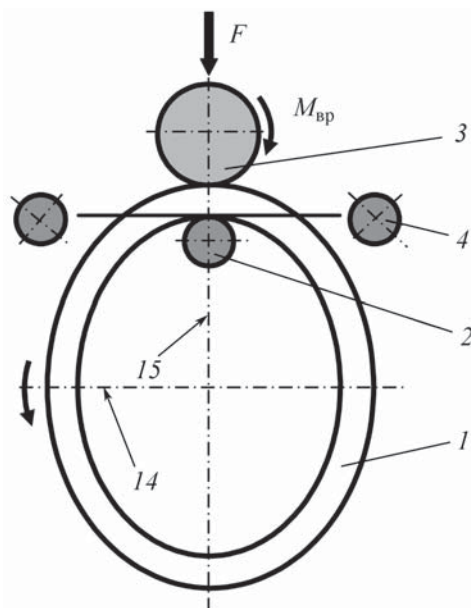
Промежуточный этап раскатки кольцевой заготовки
